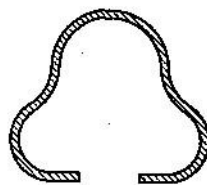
Из-за большой нагрузки при увеличенной ширине балка подвески вместительного автомобиля «Рено-эспас» получила профиль в форме клеверного листа, открытый снизу
